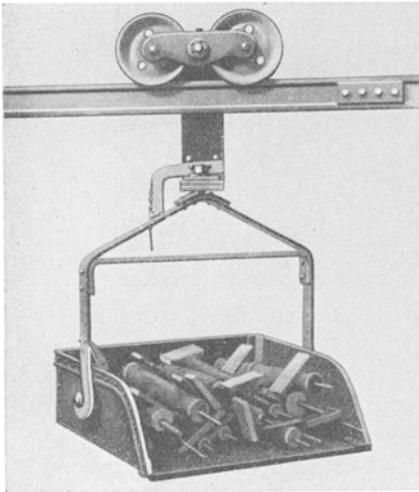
Wagen mit kippbarer Plattform. (Pohlig)
